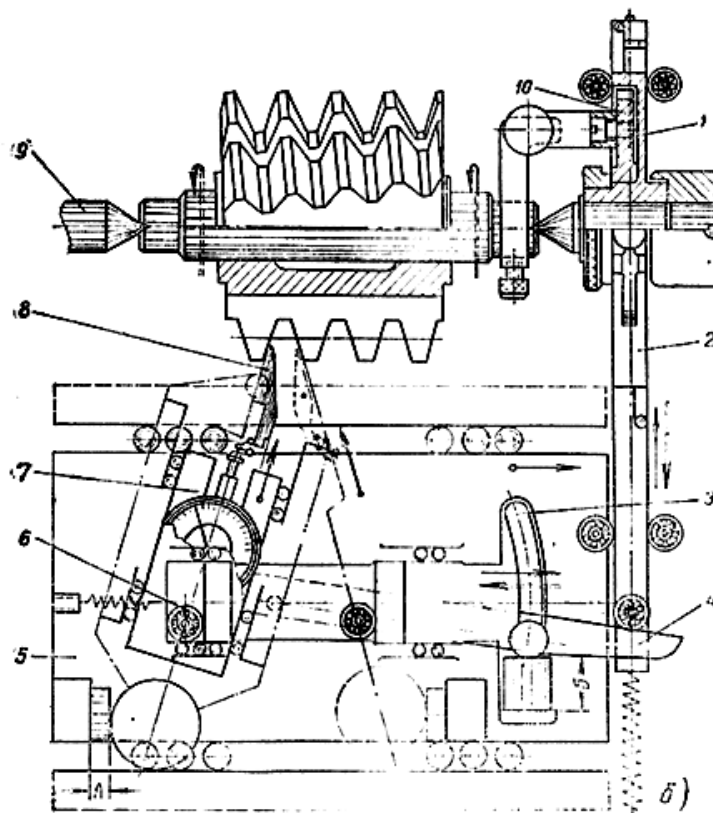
Прибор ИД для контроля червячных фрез и его кинематическая схема.
